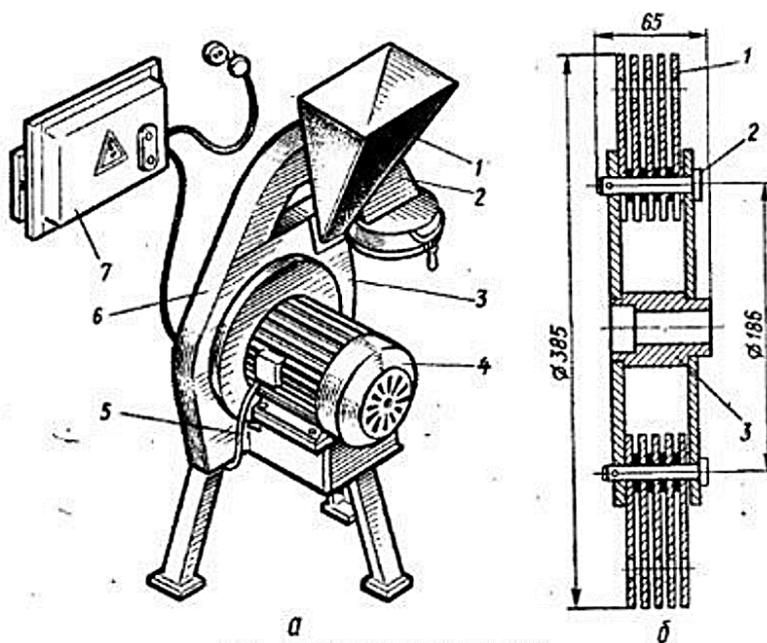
Дробарка зерна ДЗ-Т-1: а – загальний вигляд: 1 – завантажувальний бункер; 2 - вивантажувальний патрубкок; 3 – корпус; 4 - електрод-
